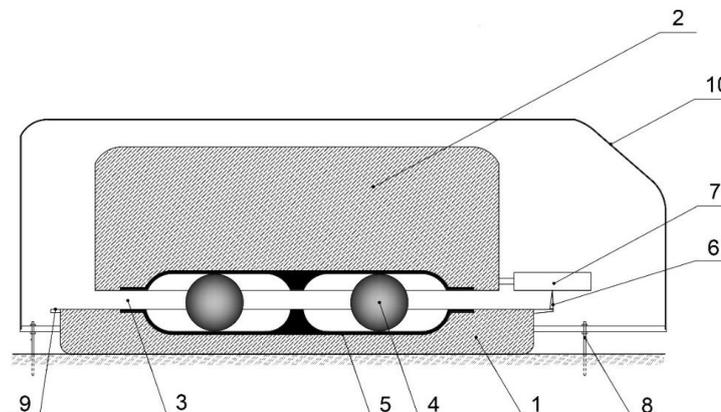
Схема сейсмографа: 1 – база корпуса; 2 – инертная масса; 3 – конструктивный зазор; 4 – металлический шар; 5 – чашевидное углубление – ячейка; 6 – подпружиненный самописец; 7 – носитель графической информации; 8 – регулируемый упор; 9 – уровень; 10 – крышка прибора
